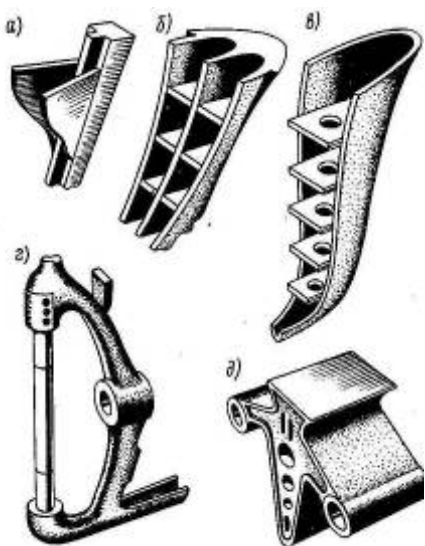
Конструктивные элементы оконечностей, а — брусковый форштевень; б — литой форштевень; в — листовой сварной форштевень; г — ахтерштевень одновинтового судна; д—выкружки гребных валов (мортиры).
